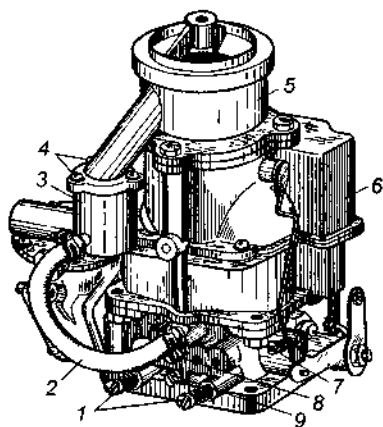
Карбюратор-смеситель К-91: 1 — винты качественной регулировки состава смеси при работе на бензине; 2 — трубка холостого хода; 3 — корпус обратного клапана; 4 — винты; 5 — переходник-смеситель; 6 — карбюратор; 7 — винт регулировки количества смеси; 8 — винт регулировки общей подачи газа в систему холостого хода; 9 — винт регулировки частоты вращения коленчатого вала на режиме холостого хода
